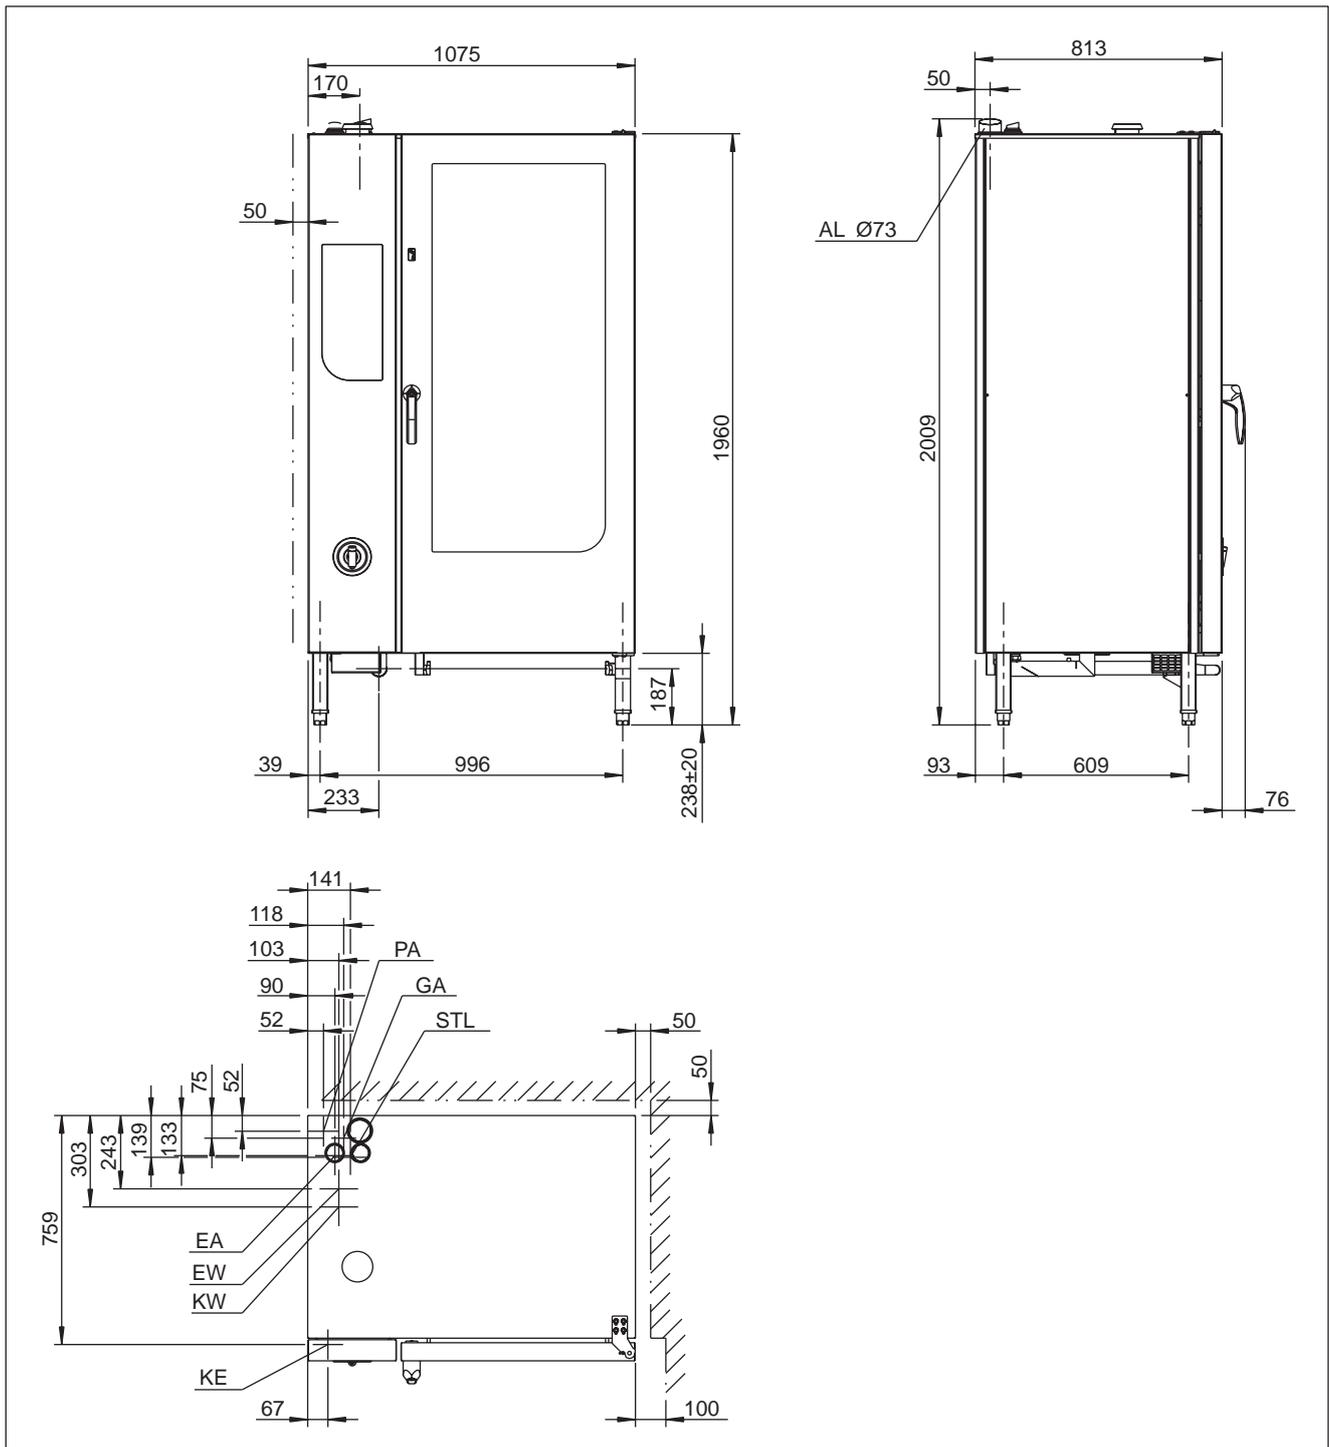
Combi-cuiseurs Henny Penny 215/220, dimensions en mm
